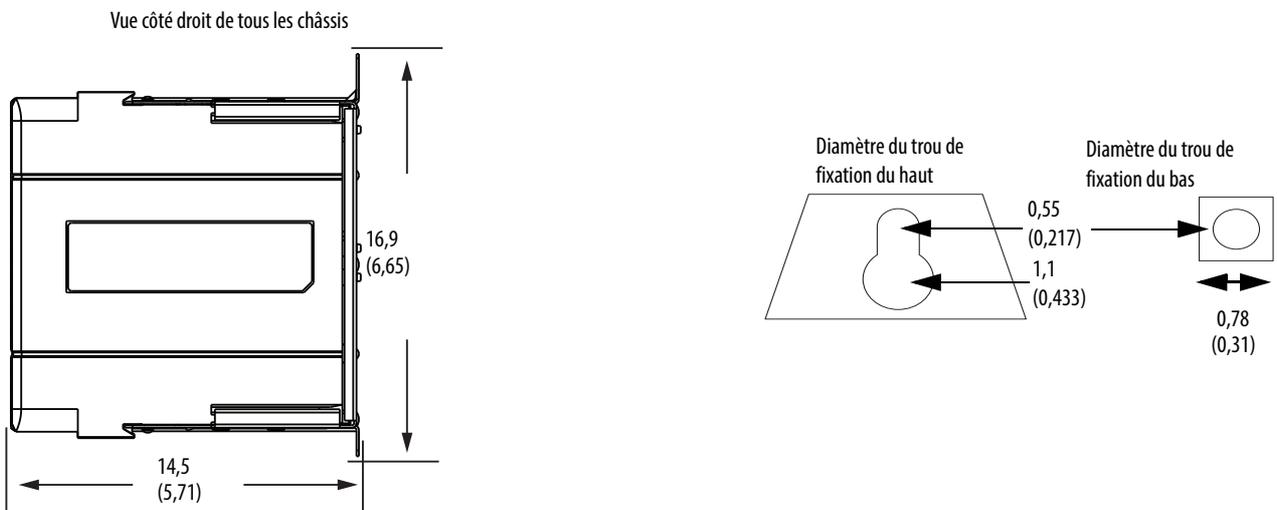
Châssis 1756-A4/B et adaptateur pour châssis
